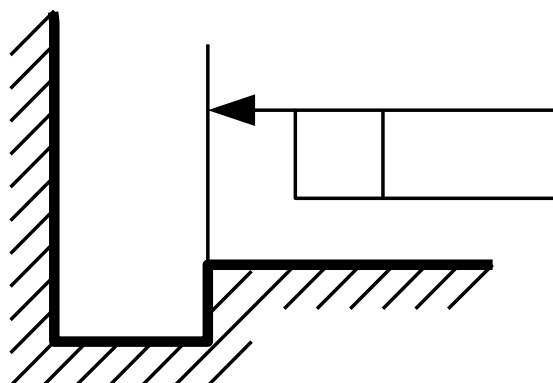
Вариант изображения условных обозначений о допусках формы и расположения поверхностей
